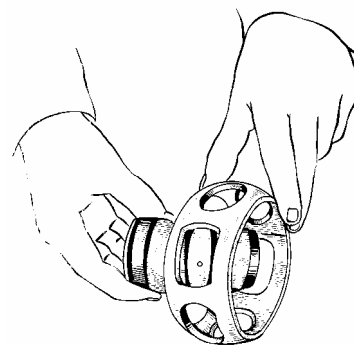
Извлечение сепаратора в сборе с обоймой из корпуса шарнира.
